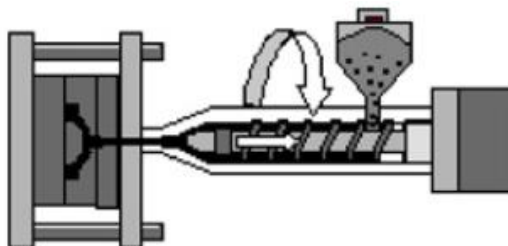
Aplicação da pós-pressão (Adaptado de [17])
